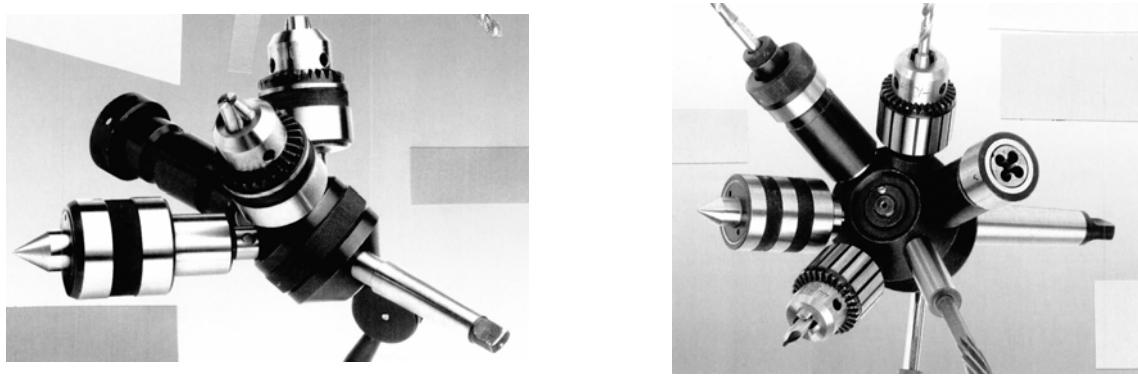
Револьверні головки з індивідуальними приводами, встановлювані в піноль задньої бабки
